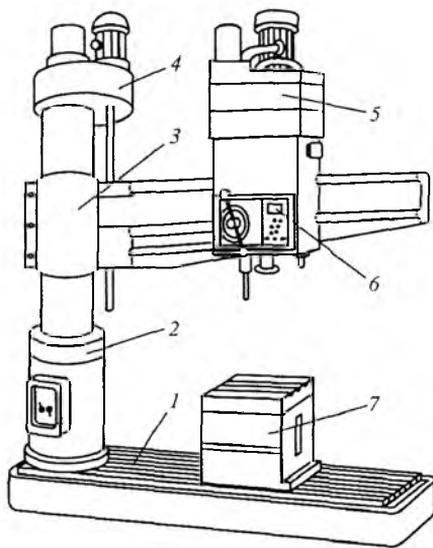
Радиально-сверлильный станок мод. 2А554:
